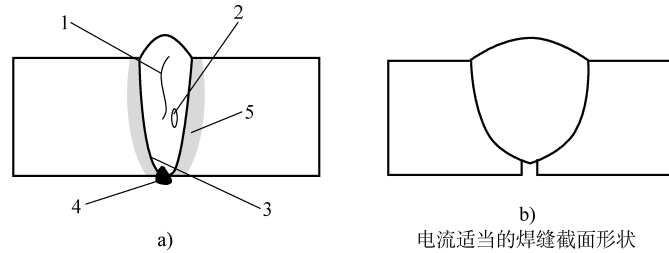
焊接电流过大可能引起的焊接缺陷
